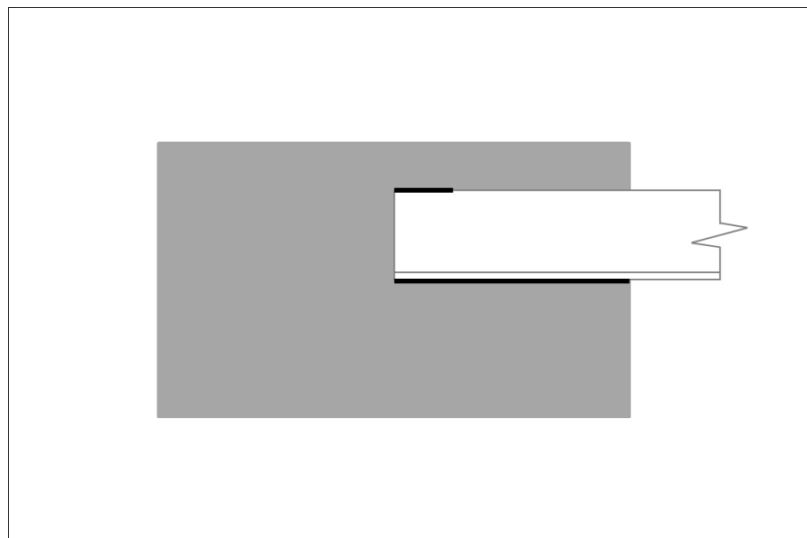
Patrón de soldadura utilizado en el caso 3.
